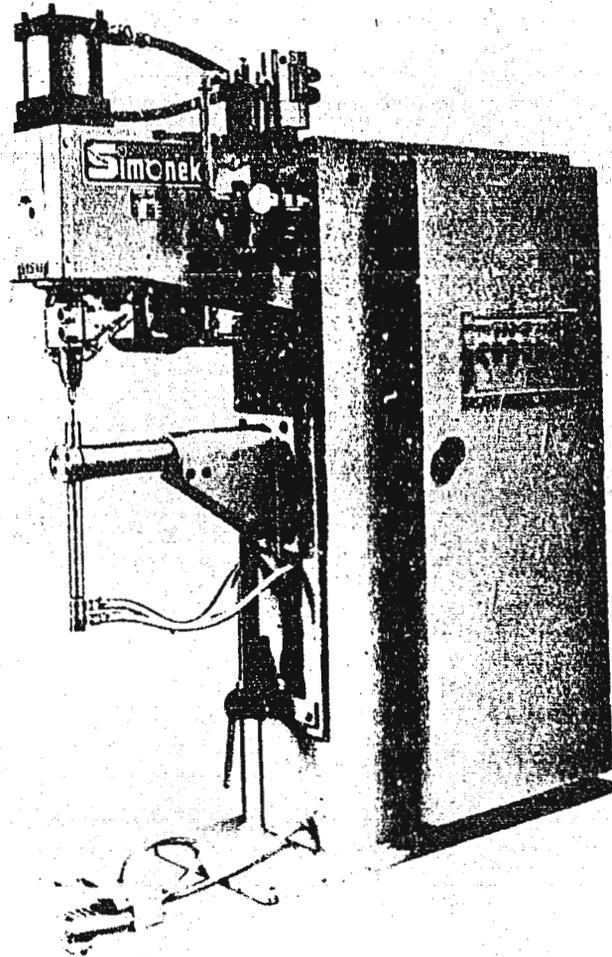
Máquina estacionaria para soldadura por puntos.
